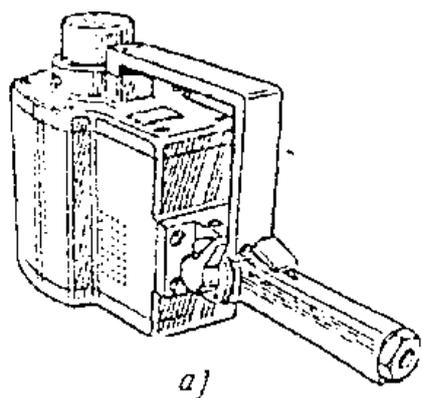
Стяжка –распорка пневматическая СПУ-10.
